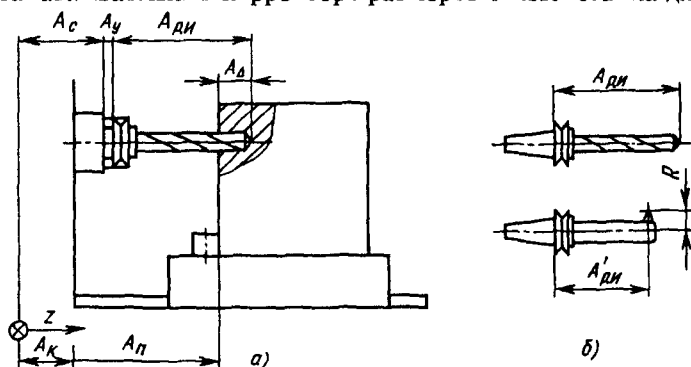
Влияние размера настройки режущего инструмента на размер детали: а — схема операционной размерной цепи; б — размер инструментов
